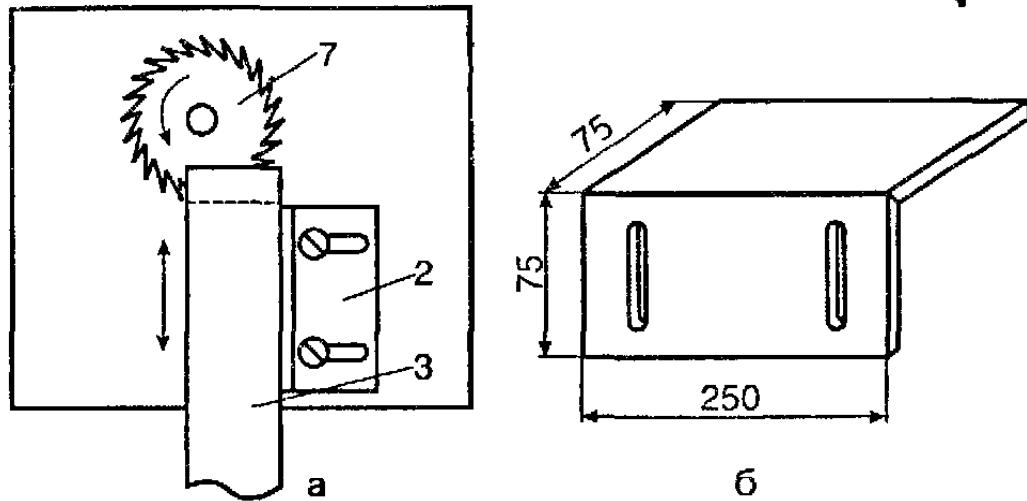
Схема фрезерования шипов в пятой и четвертой позициях станка с помощью опорного уголка:
